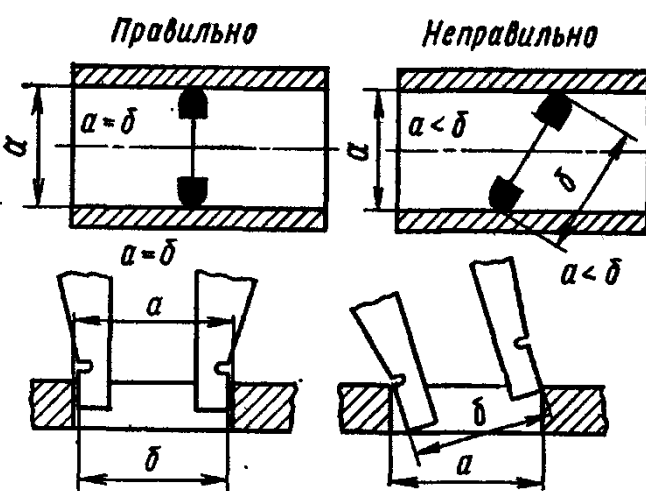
Установка штангенциркуля при измерении внутренних поверхностей
